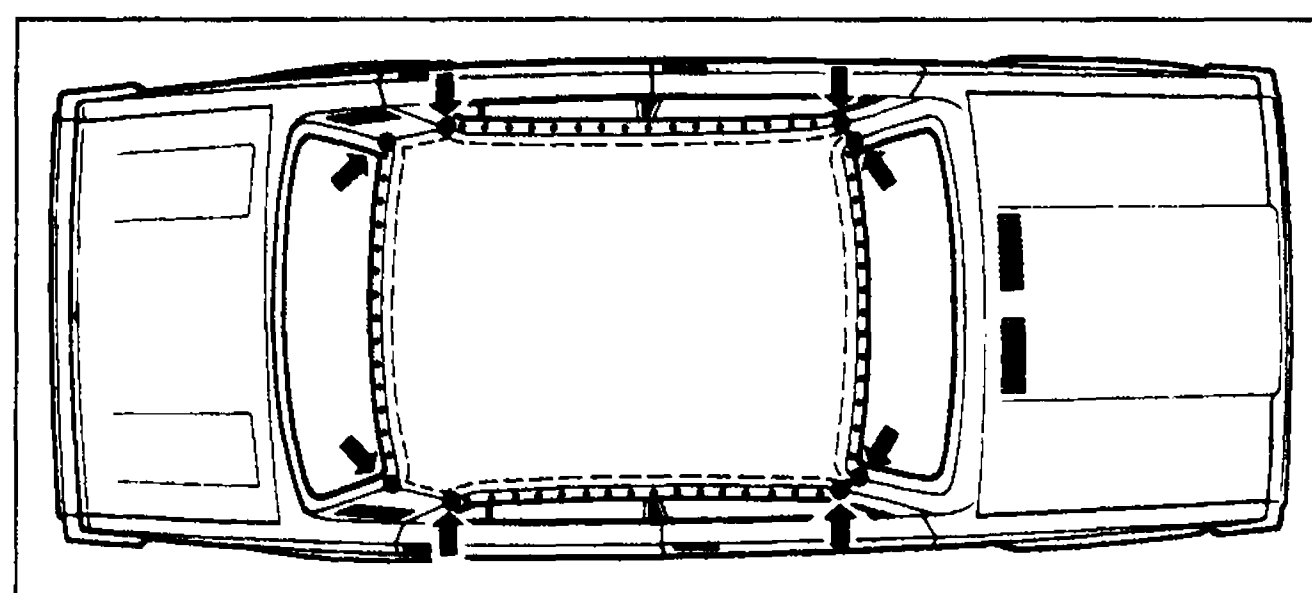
Места сварки крыши. Точками обозначены швы контактной сварки. Стрелками показаны места газовой сварки.
